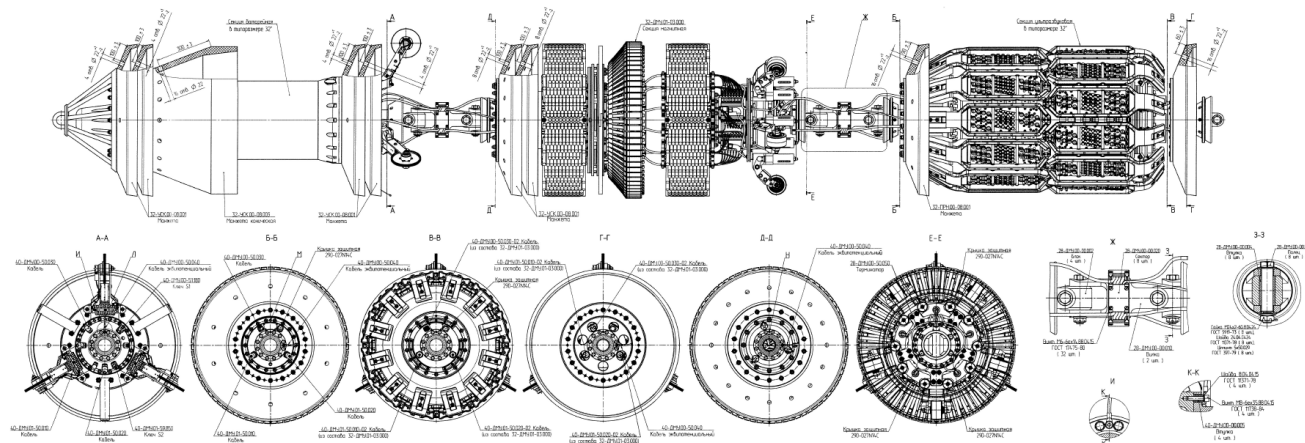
Чертеж общего вида дефектоскопа внутритрубного комбинированного магнитно-ультразвукового 28-ДМУ.01-00.000 в типоразмере 820 мм (32" API)
